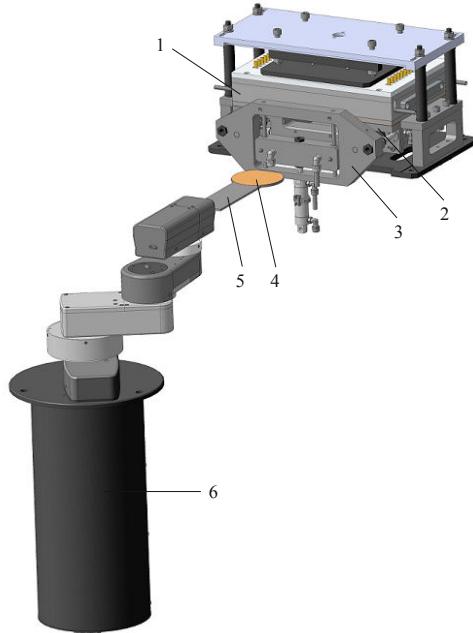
Загрузка полупроводниковой пластины роботизированным комплексом в камеру отжига установки быстрой термообработки: 1 – блок нагрева, 2 – камера отжига, 3 – затвор, 4 – полупроводниковая пластина, 5 – подложкодержатель, 6 – робот-манипулятор
